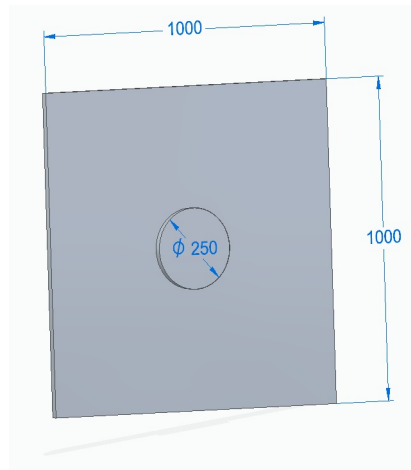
Base - základná konštrukcia zväracieho stola.
